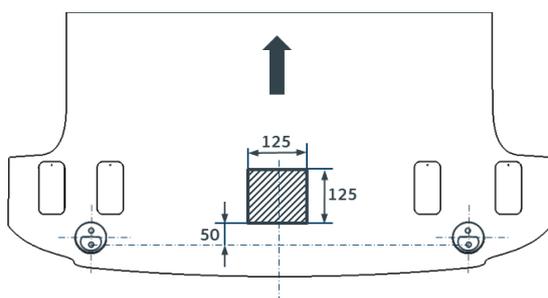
posizione e apertura per la bocchetta a pavimento sulla parte posteriore della vettura (quote in mm)
